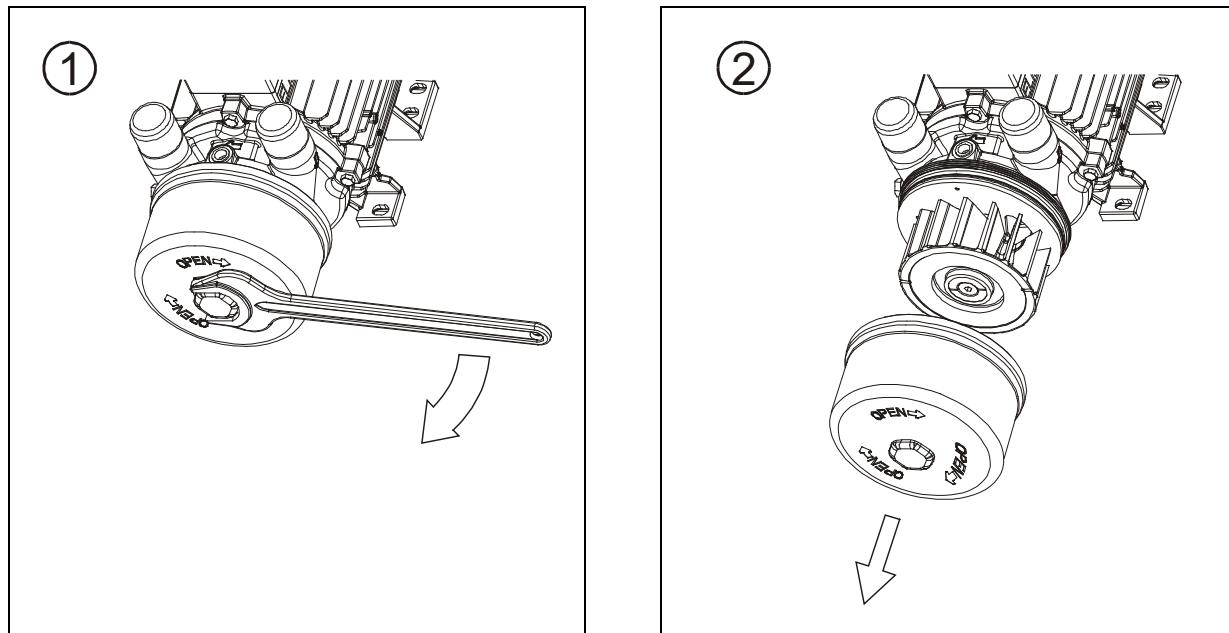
Demontage des Vakumpumpen- / Kompressoren-Gehäuses
